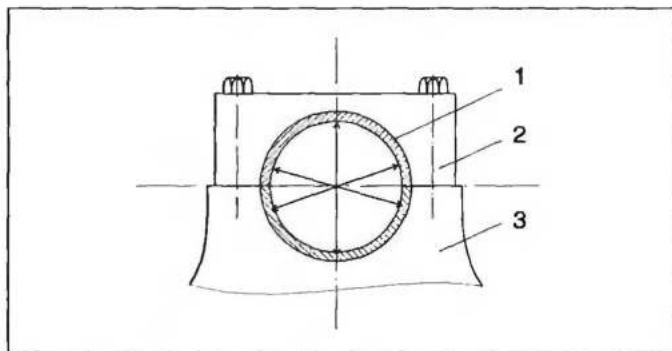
Схема проверки внутреннего диаметра подшипника коленчатого вала:
